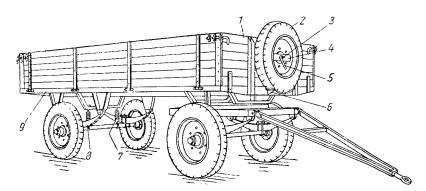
Двухосный прицеп с бортовым кузовом.
